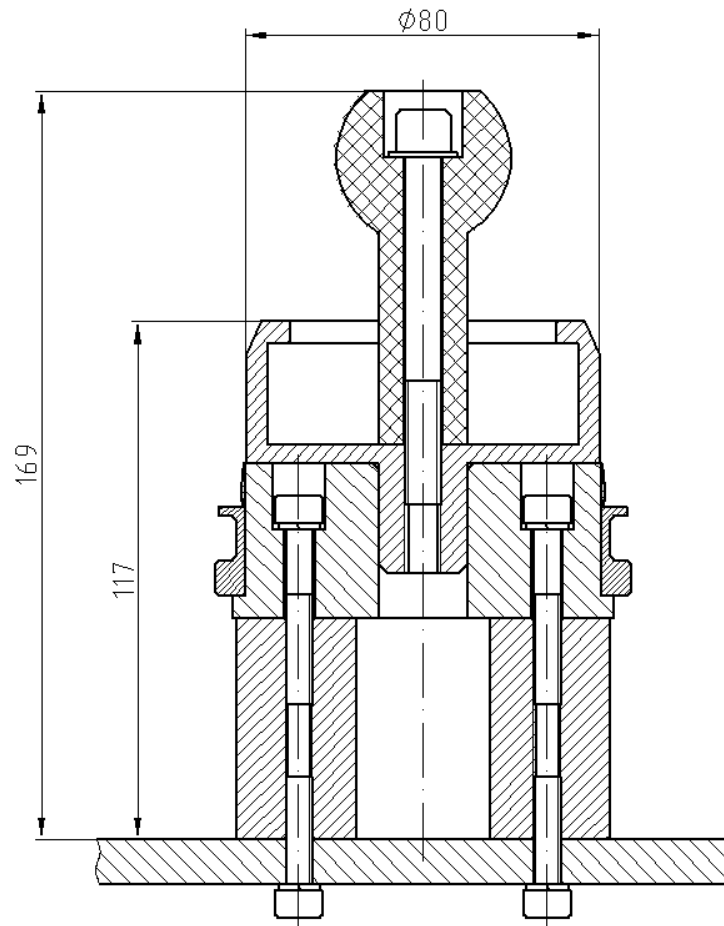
3M 7820-4733, Werkzeug zum Einbau des Stopfbuchshalters mit Stopfbuchse ohne Feder
